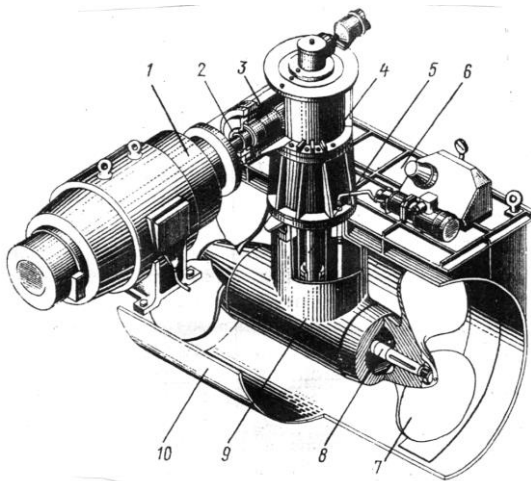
Подруливающее устройство с парными винтами противоположного вращения: 1 – реверсивный электродвигатель, 2 – эластичная муфта, 3 – ведущий вал, 4 – верхний редуктор, 5 – вертикальный вал, 6 – опорная плита, 7 – гребной винт, 8 – гребной вал, 9 – нижний редуктор, 10 – поперечный туннель
